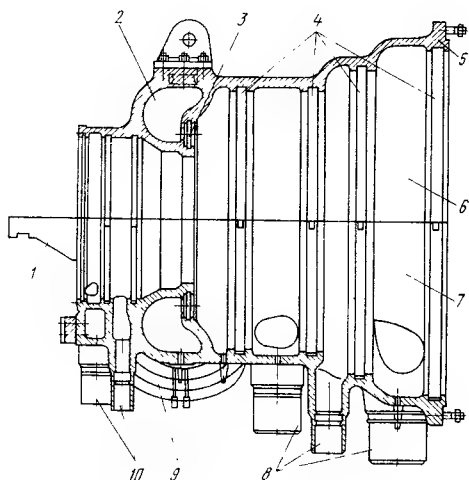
Конструкция передней части корпуса ЦСД турбины К-300-240 ЛМЗ:
